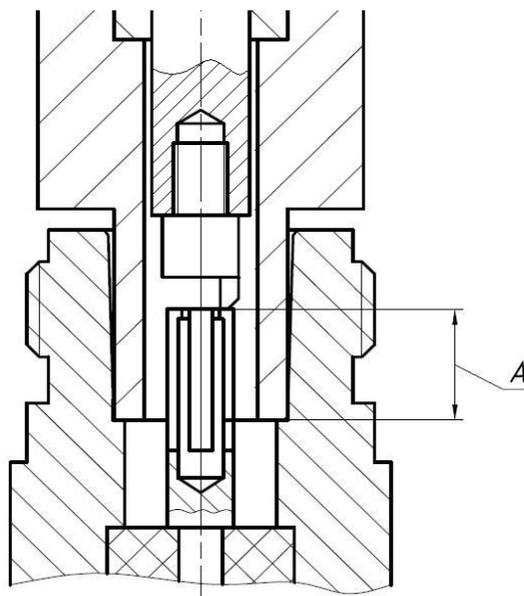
Проверка размера «А» соединителя «розетка»
